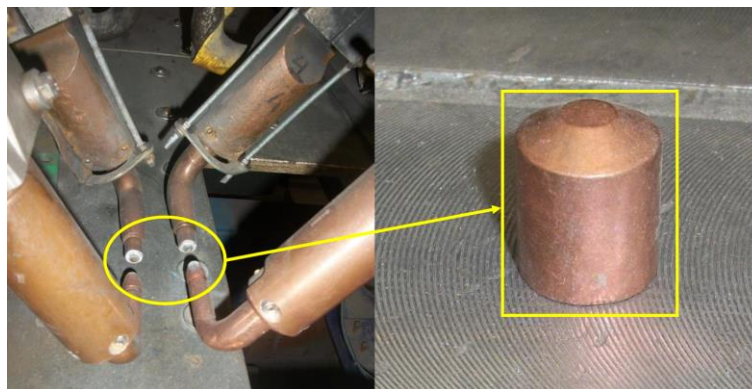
Brazos de la máquina de soldadura y electrodos empleados
